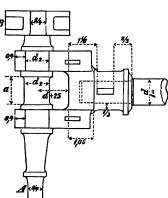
geschmiedeter Kreuzkopf für grosse liegende Maschinen. — Ende B gilt für Maschinen, deren Cylinder auf einer Fundamentplatte ruht, A dagegen für Cylinder, welche zwischen zwei Rahmen liegen, wie häufig bei Gebläsen, Wasserhaltungsmaschinen etc.
